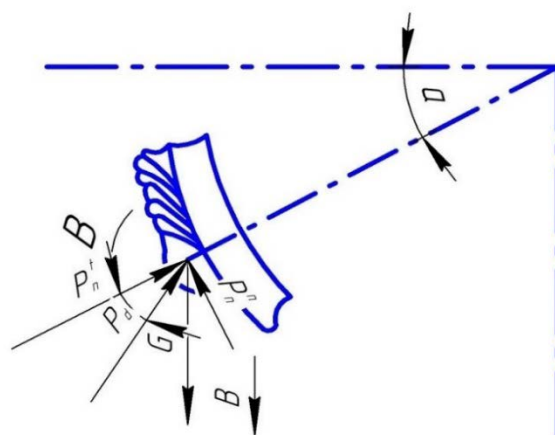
Силы, действующие на сварочную ванну при работе с углами от 90⁰-180⁰
